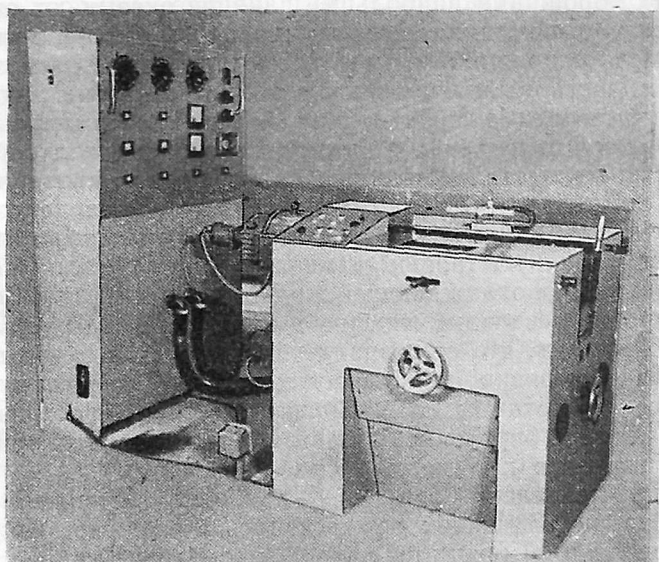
Универсальный станок для магнитно-абразивной обработки цилиндрических деталей мод. МАС-1А
